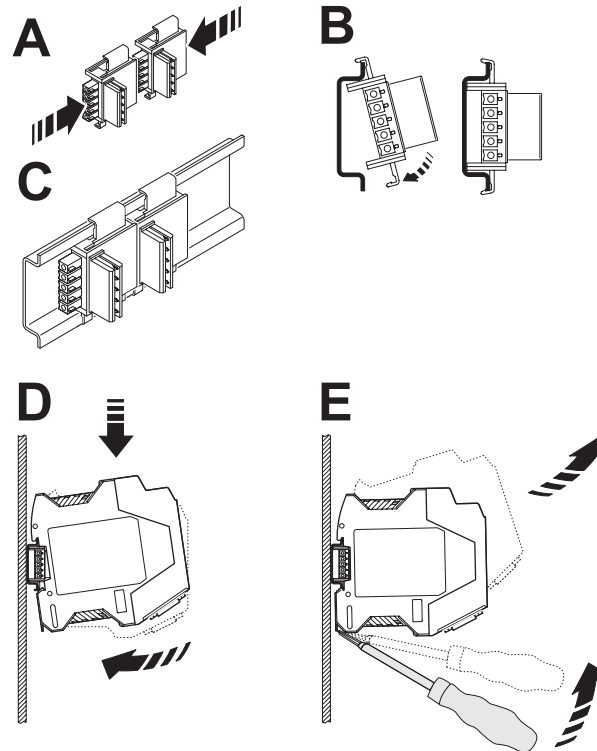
Montaggio e smontaggio della stazione di collegamento
